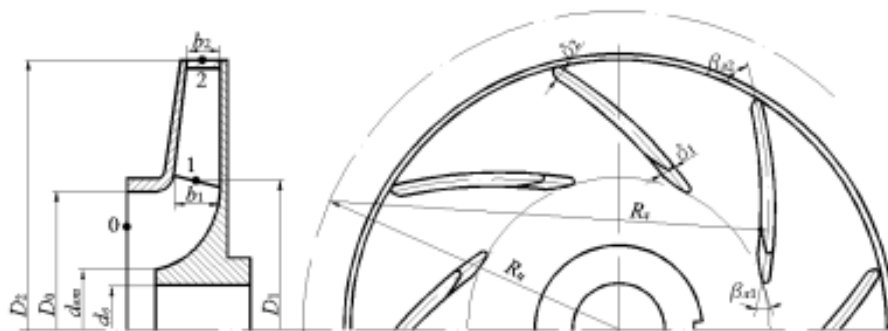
Общий вид рассчитанного ротора диспергатора
